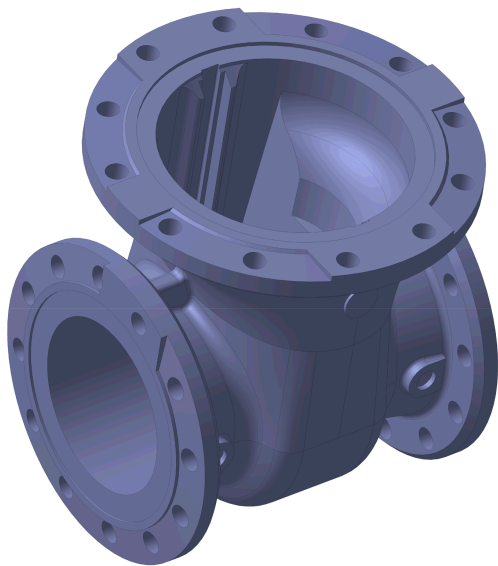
3D-модель детали «Водозапорный клапан»
